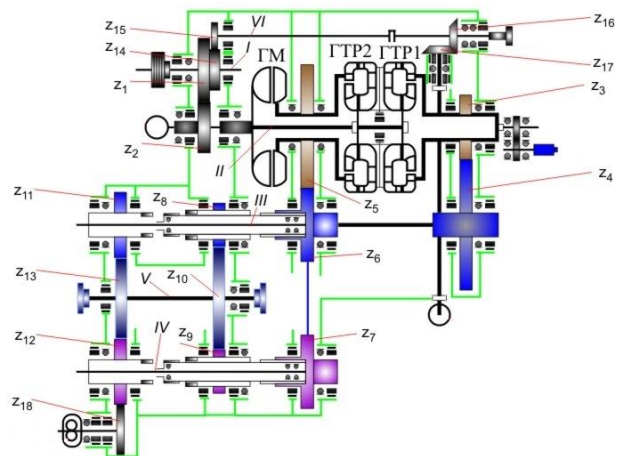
Кинематическая схема УГП 750/1200: ГТР1 – пусковой гидротрансформатор; ГТР2 – маршевый гидротрансформатор; ГМ – гидромуфта; z_1 - z_{18} – зубчатые колеса; I – входной вал; II – главный вал; III – вторичный вал; IV – вал реверса; V – раздаточный вал; VI – вал отбора мощности
